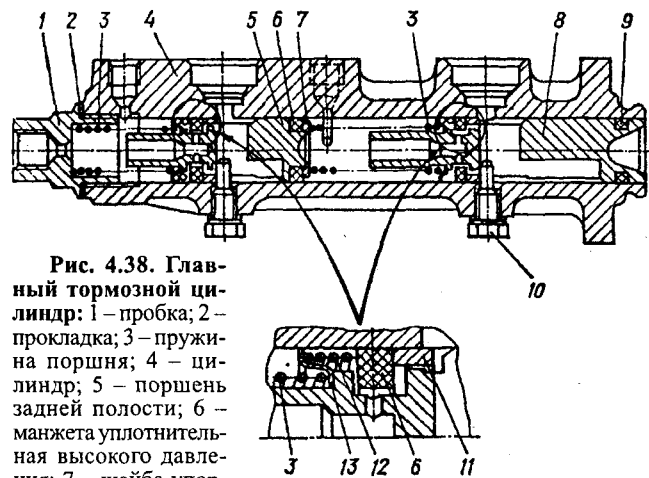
Главный тормозной цилиндр: 1 — пробка; 2 — прокладка; 3 — пружина поршня; 4 — цилиндр; 5 — поршень задней полости; 6 — манжета уплотнительная высокого давления; 7 — шайба упорная; 8 — поршень передней полости; 9 — манжета уплотнительная низкого давления; 10 — болт установочный; 11 — втулка распорная; 12 — пружина чашки; 13 — чашка
